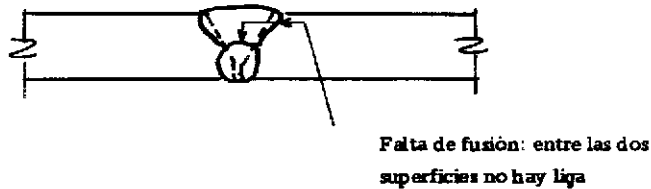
Junta soldada con falta de fusión.
